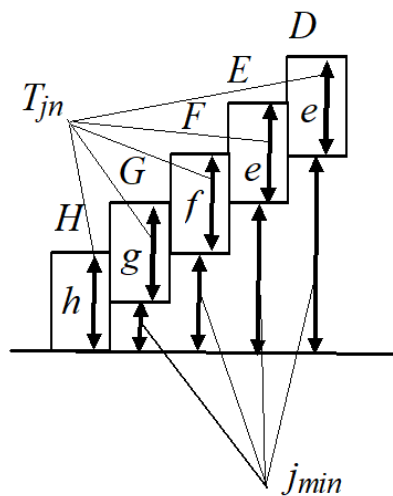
Расположение полей допусков боковых зазоров
